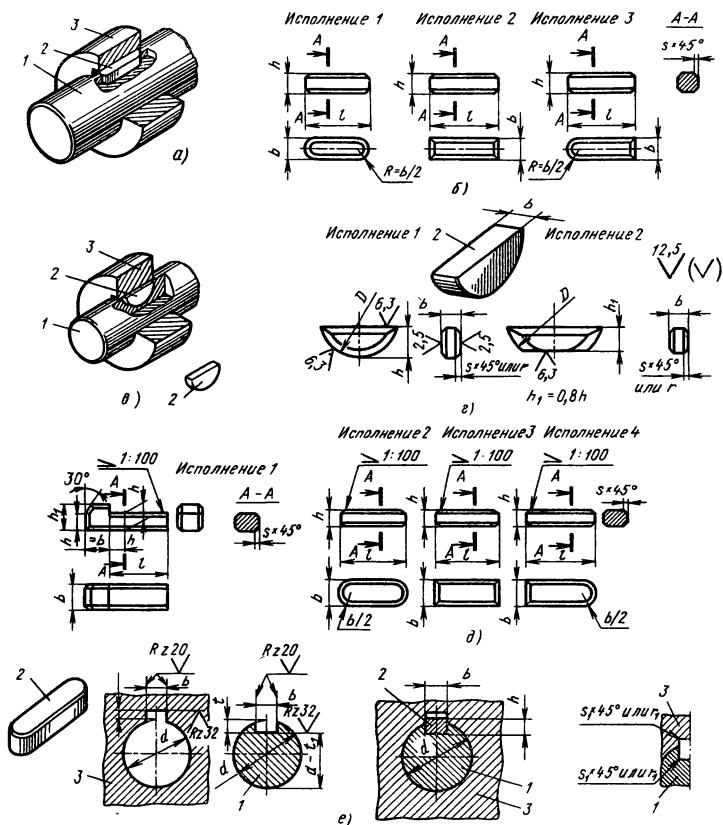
Шпоночное соединение с призматической и сегментной шпонками; 1 – вал; 2 – шпонка; 3 – втулка (ступица)
